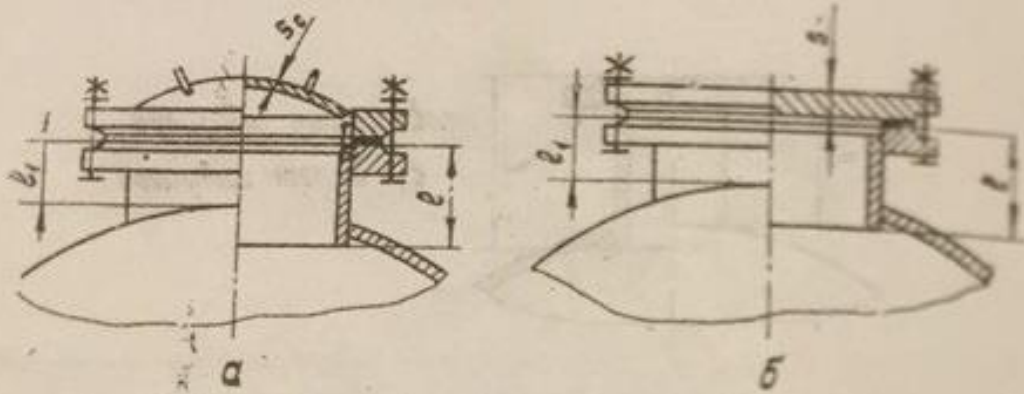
Конструкции люков: а — со сферической крышкой; б — с плоской крышкой.
